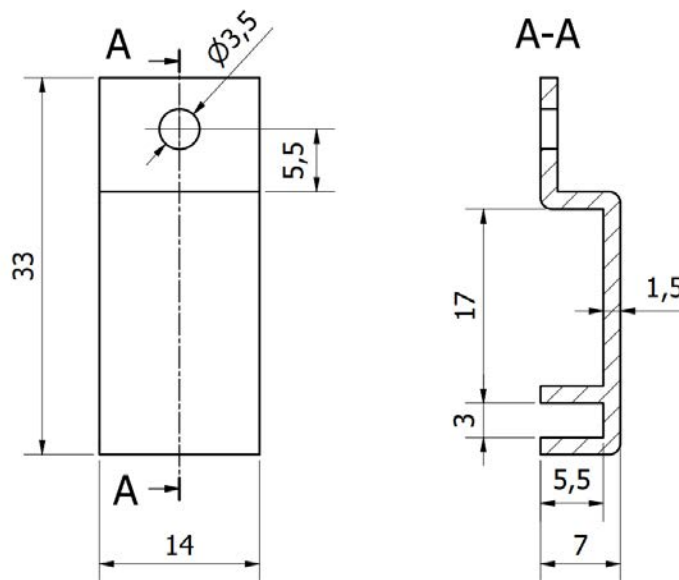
Dimensiones en mm de las piezas de anclaje de las cubiertas de protección para los Minicrates.
